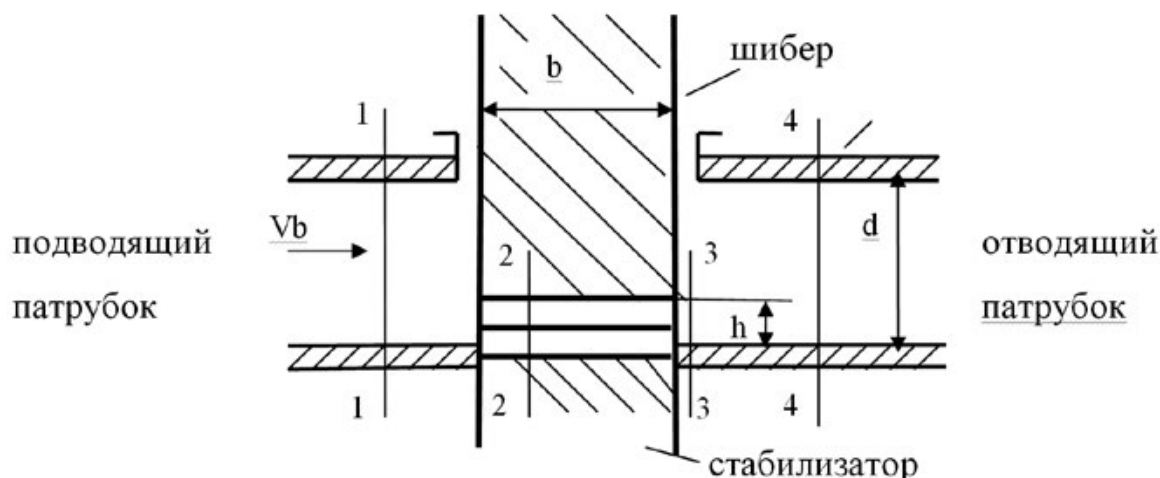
Схема шиберной запорно-регулирующей задвижки со стабилизатором; d — диаметр трубы, b — толщина шибера и длина зазора, h — ход шибера
